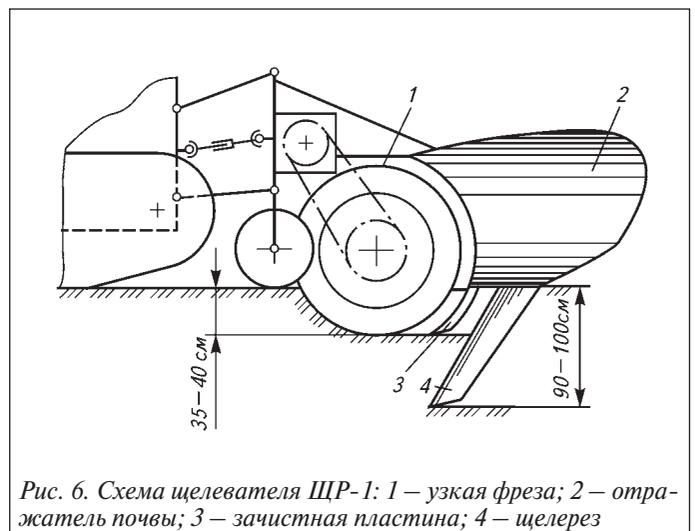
Схема щелевателя ЩР-1: 1 – узкая фреза; 2 – отражатель почвы; 3 – зачистная пластина; 4 – щелерез
